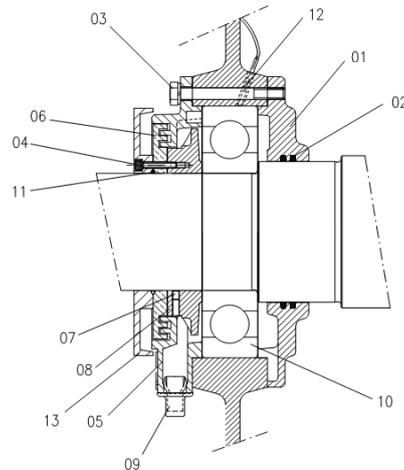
Детали подшипника качения с консистентной смазкой
